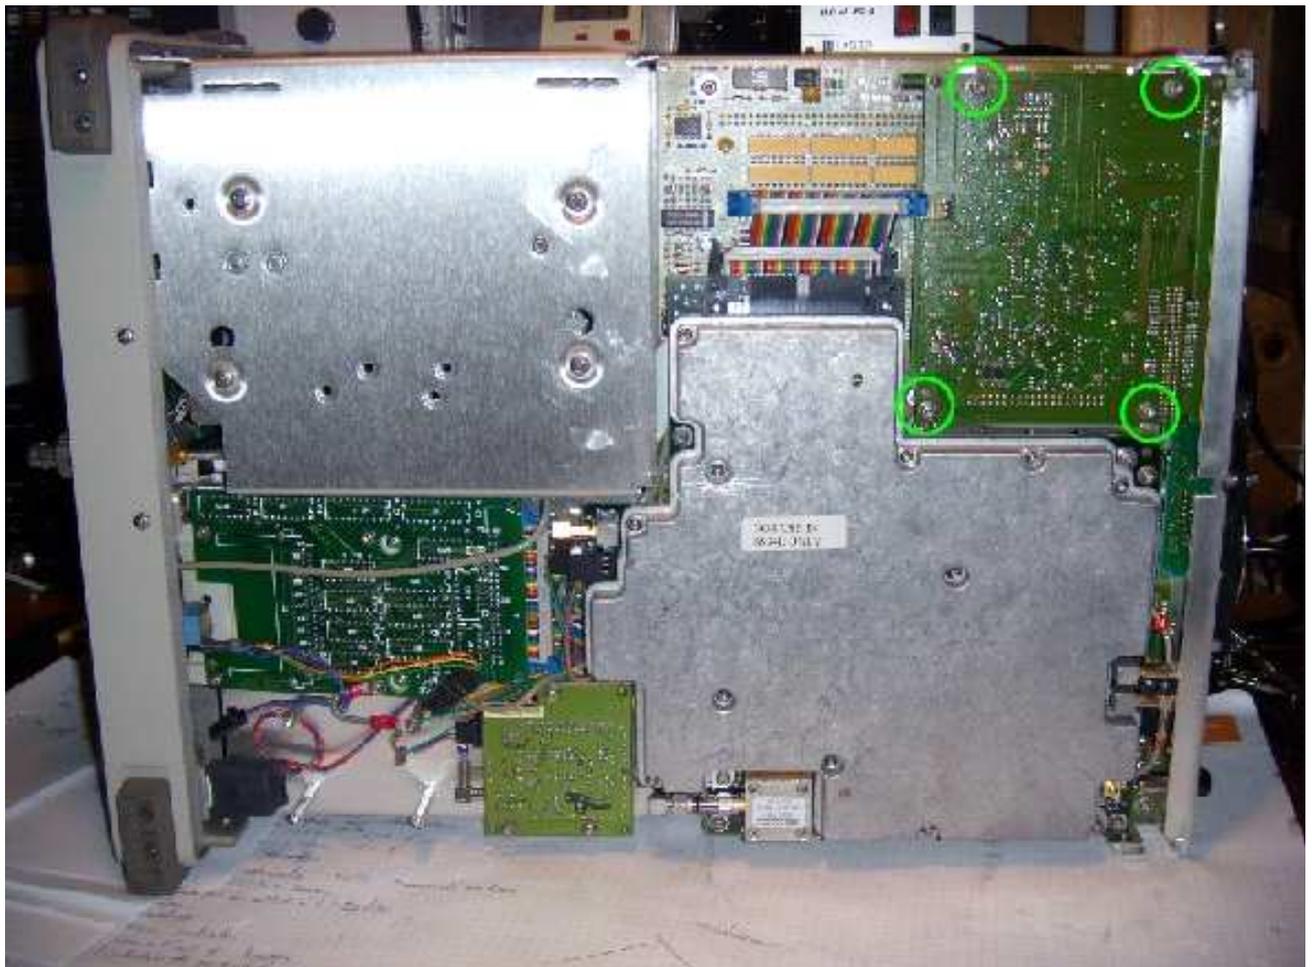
Un premier circuit à démonter pour accéder au PCB des RAM.
